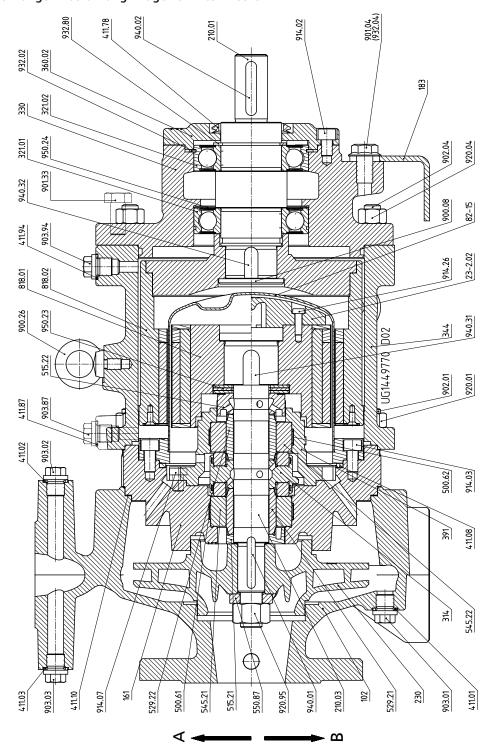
Gesamtzeichnung Ausführung mit geklemmtem Deckel ohne Zwischenstück
